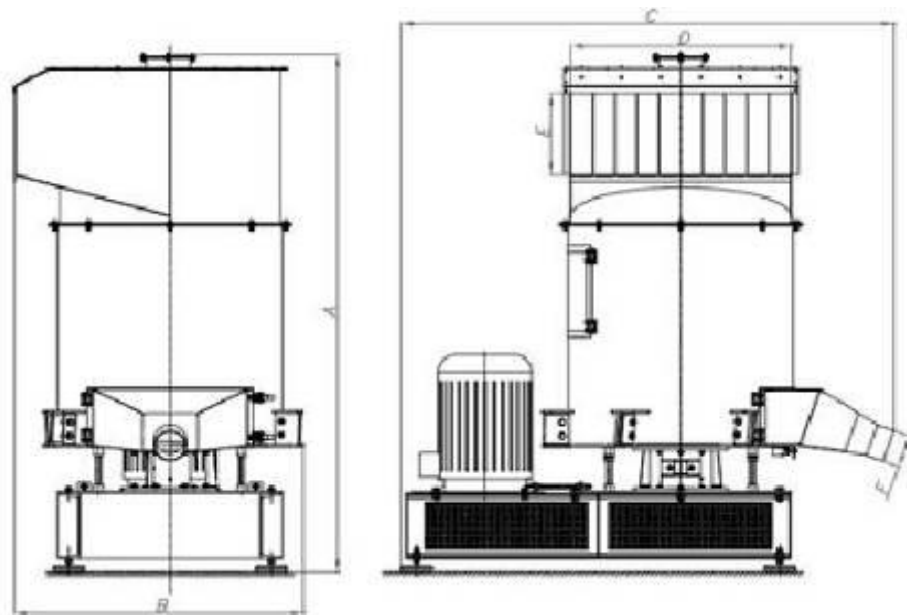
Дробарка з вертикальною віссю обертання ротора
